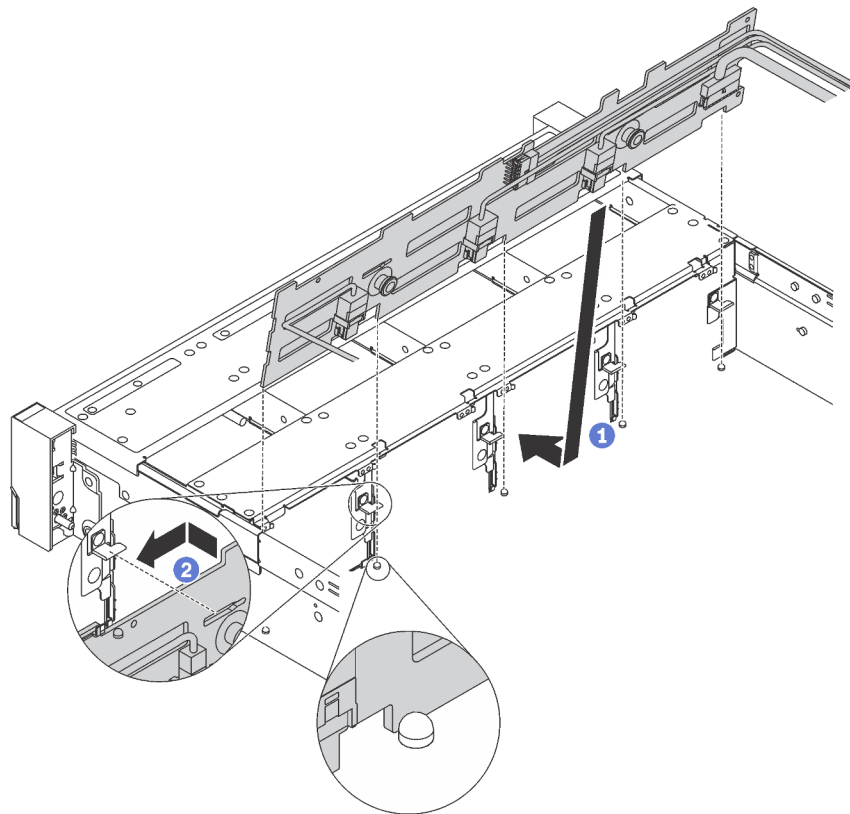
Installation d'un fond de panier d'unité 3,5 pouces
